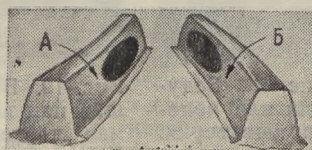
Контакт зуба ведомой шестерни под легкой нагрузкой или без нагрузки.
